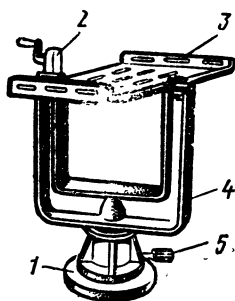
Поворотный стенд для сборки небольших изделий: станина 4 поворачивается на вертикальной оси в массивном основании 1 и закрепляется педалью 5; на цапфах станины укреплен стол 3, на котором устанавливается изделие; редуктором 2 стол поворачивают вручную вокруг горизонтальной оси на 360° .
